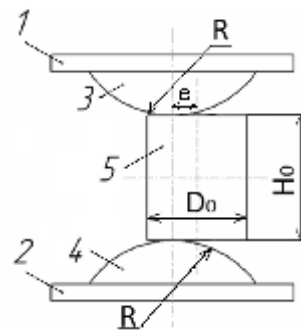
Схема эксцентричной осадки заготовки радиусными бойками:
